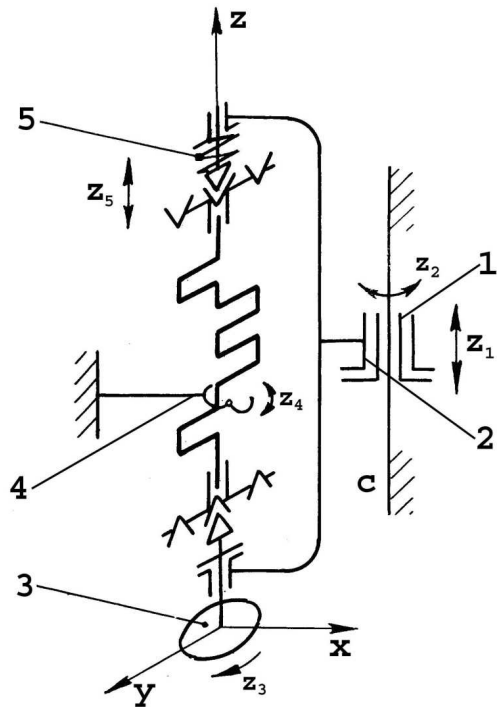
Схема станда для закалки шеек коленчатого вала: С – станина; 1 – механизм осевого перемещения детали; 2 – механизм введения шейки вала в индуктор; 3 – механизм вращения детали; 4 – индуктор; 5 – пиноль
